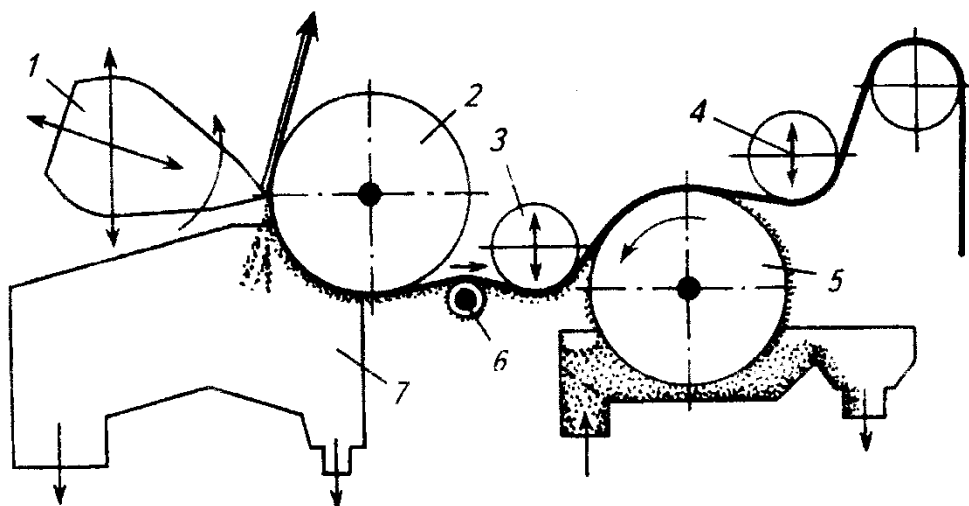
Схема нанесения покрытия с использованием воздушного шабера:
